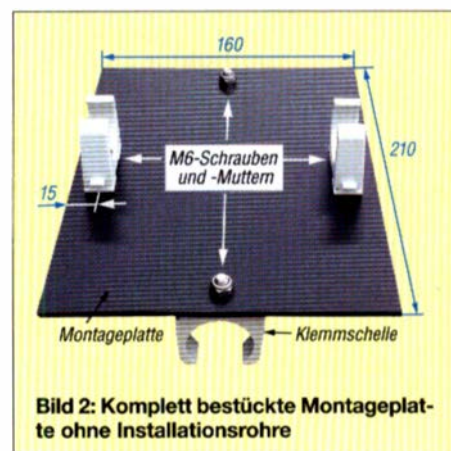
Komplett bestückte Montageplatte ohne Installationsrohre
